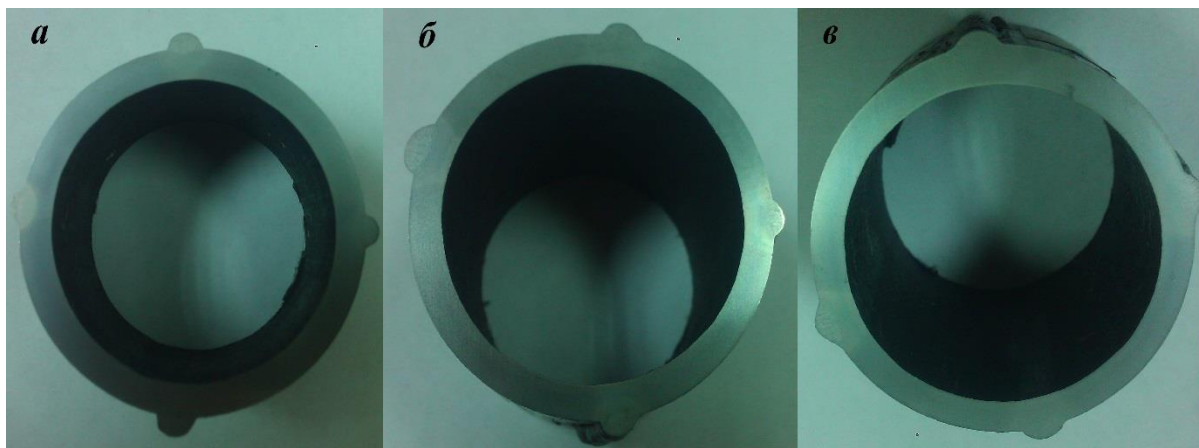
Образцы: а – наплавка металла при силе тока 60 А.; б – наплавка металла при силе тока 80 А.; в – наплавка металла при силе тока 100 А.
